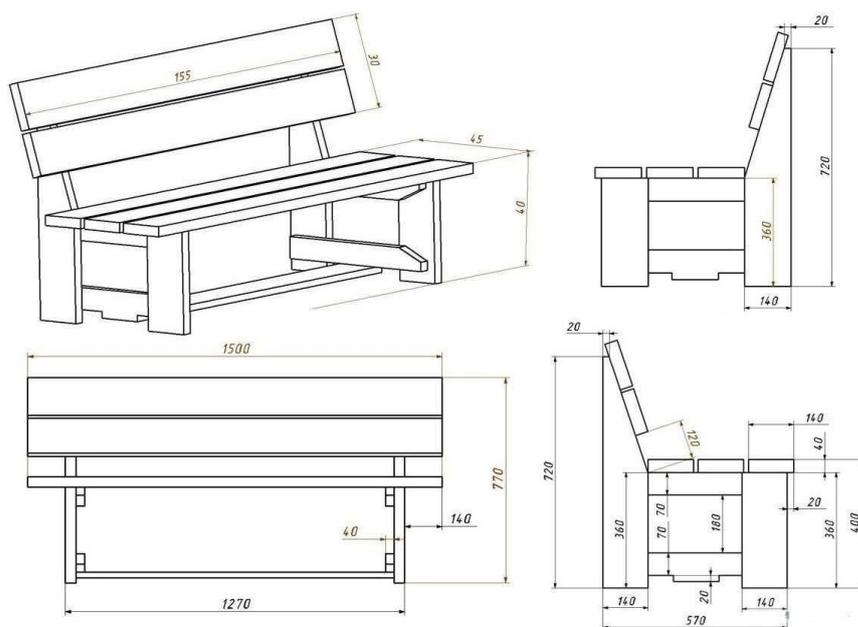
Пример выполнения эскизного чертежа нетипового изделия (уличная скамья)
